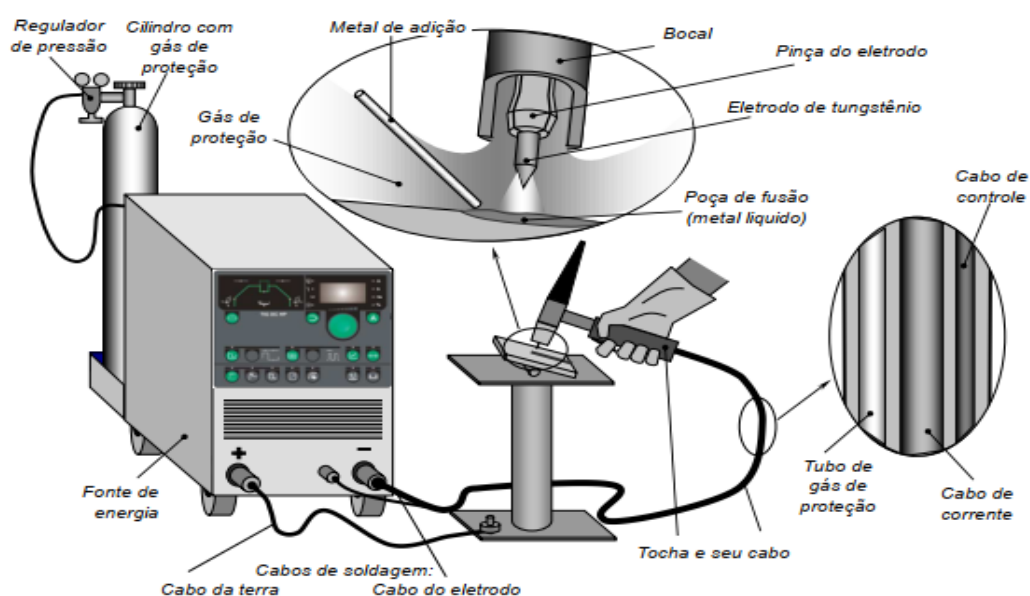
Soldagem TIG. Fonte: Prof. Dr. Volodymyr Ponomarov
